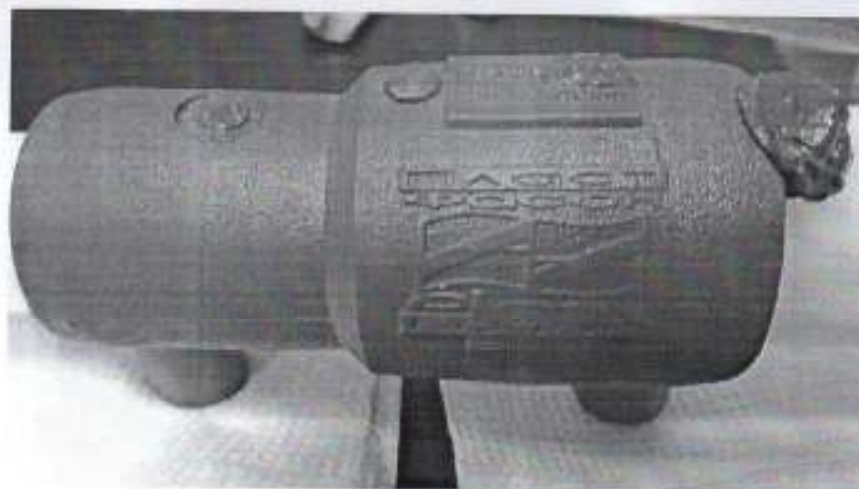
Руйнування переходу редукційного в процесі зварювання
